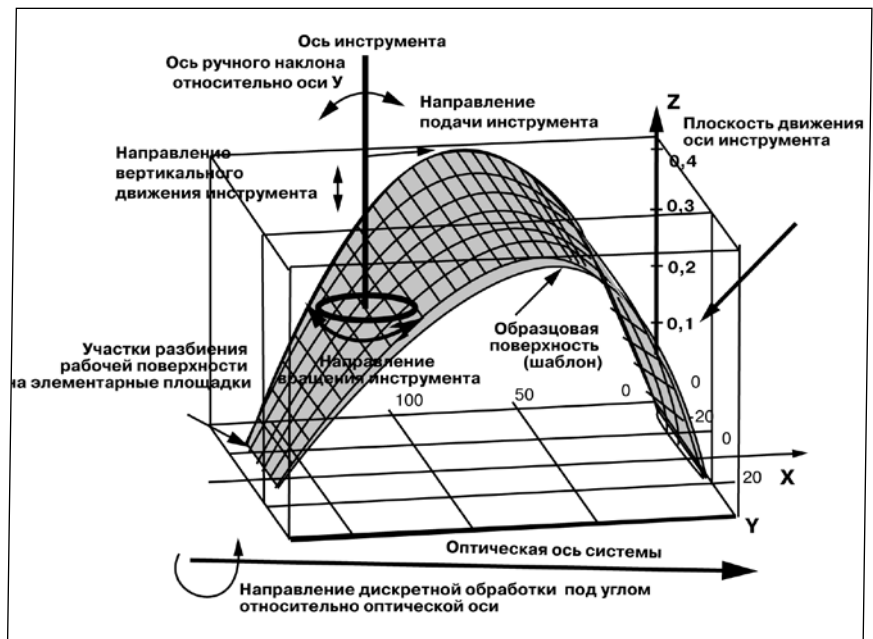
Общая схема обработки цилиндрической поверхности методом полирования малоразмерным инструментом
